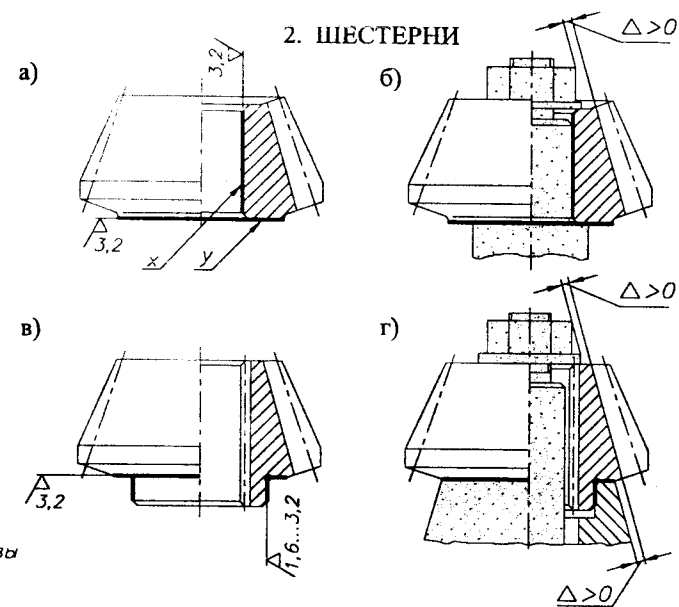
Установочные базы для нарезания зубьев на шестернях
